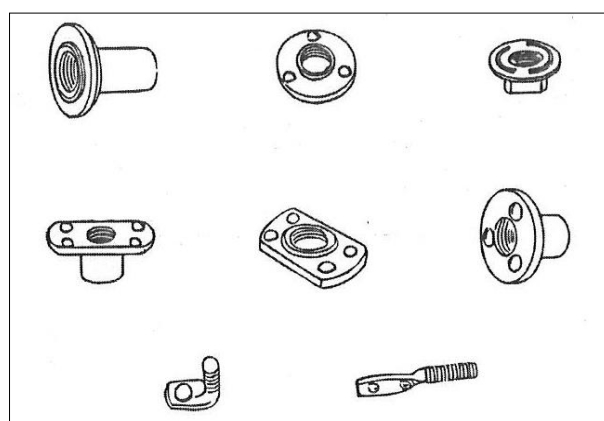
Piezas auxiliares que son pasibles de ser soldadas por proyección y ser tratadas como tuercas.
